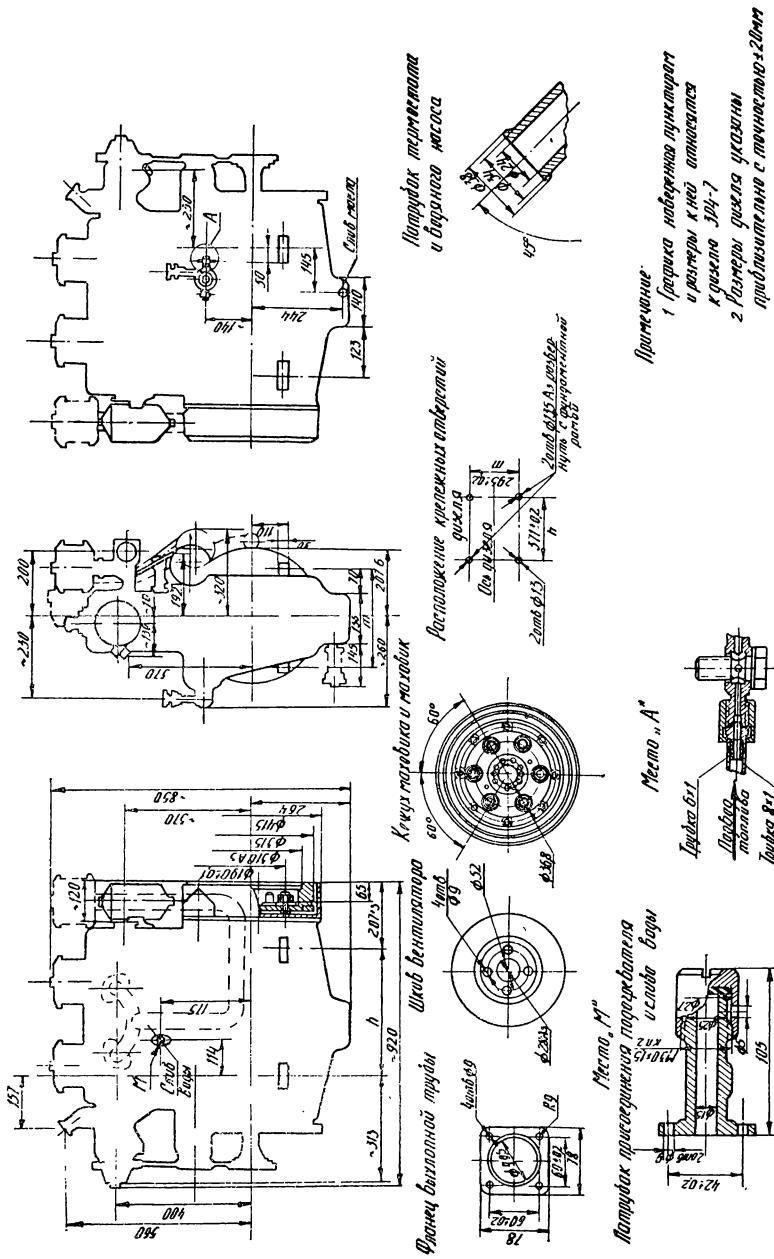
Габаритный чертеж дизеля 2 Ч 8,5/11 (4Р2-6).
